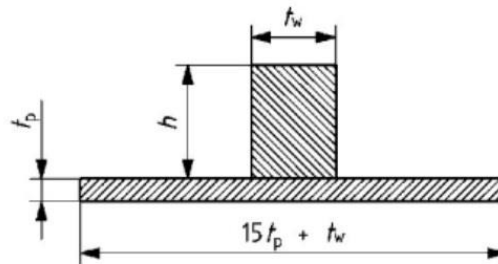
Geometría de los refuerzos (Fuente: ISO12215)
